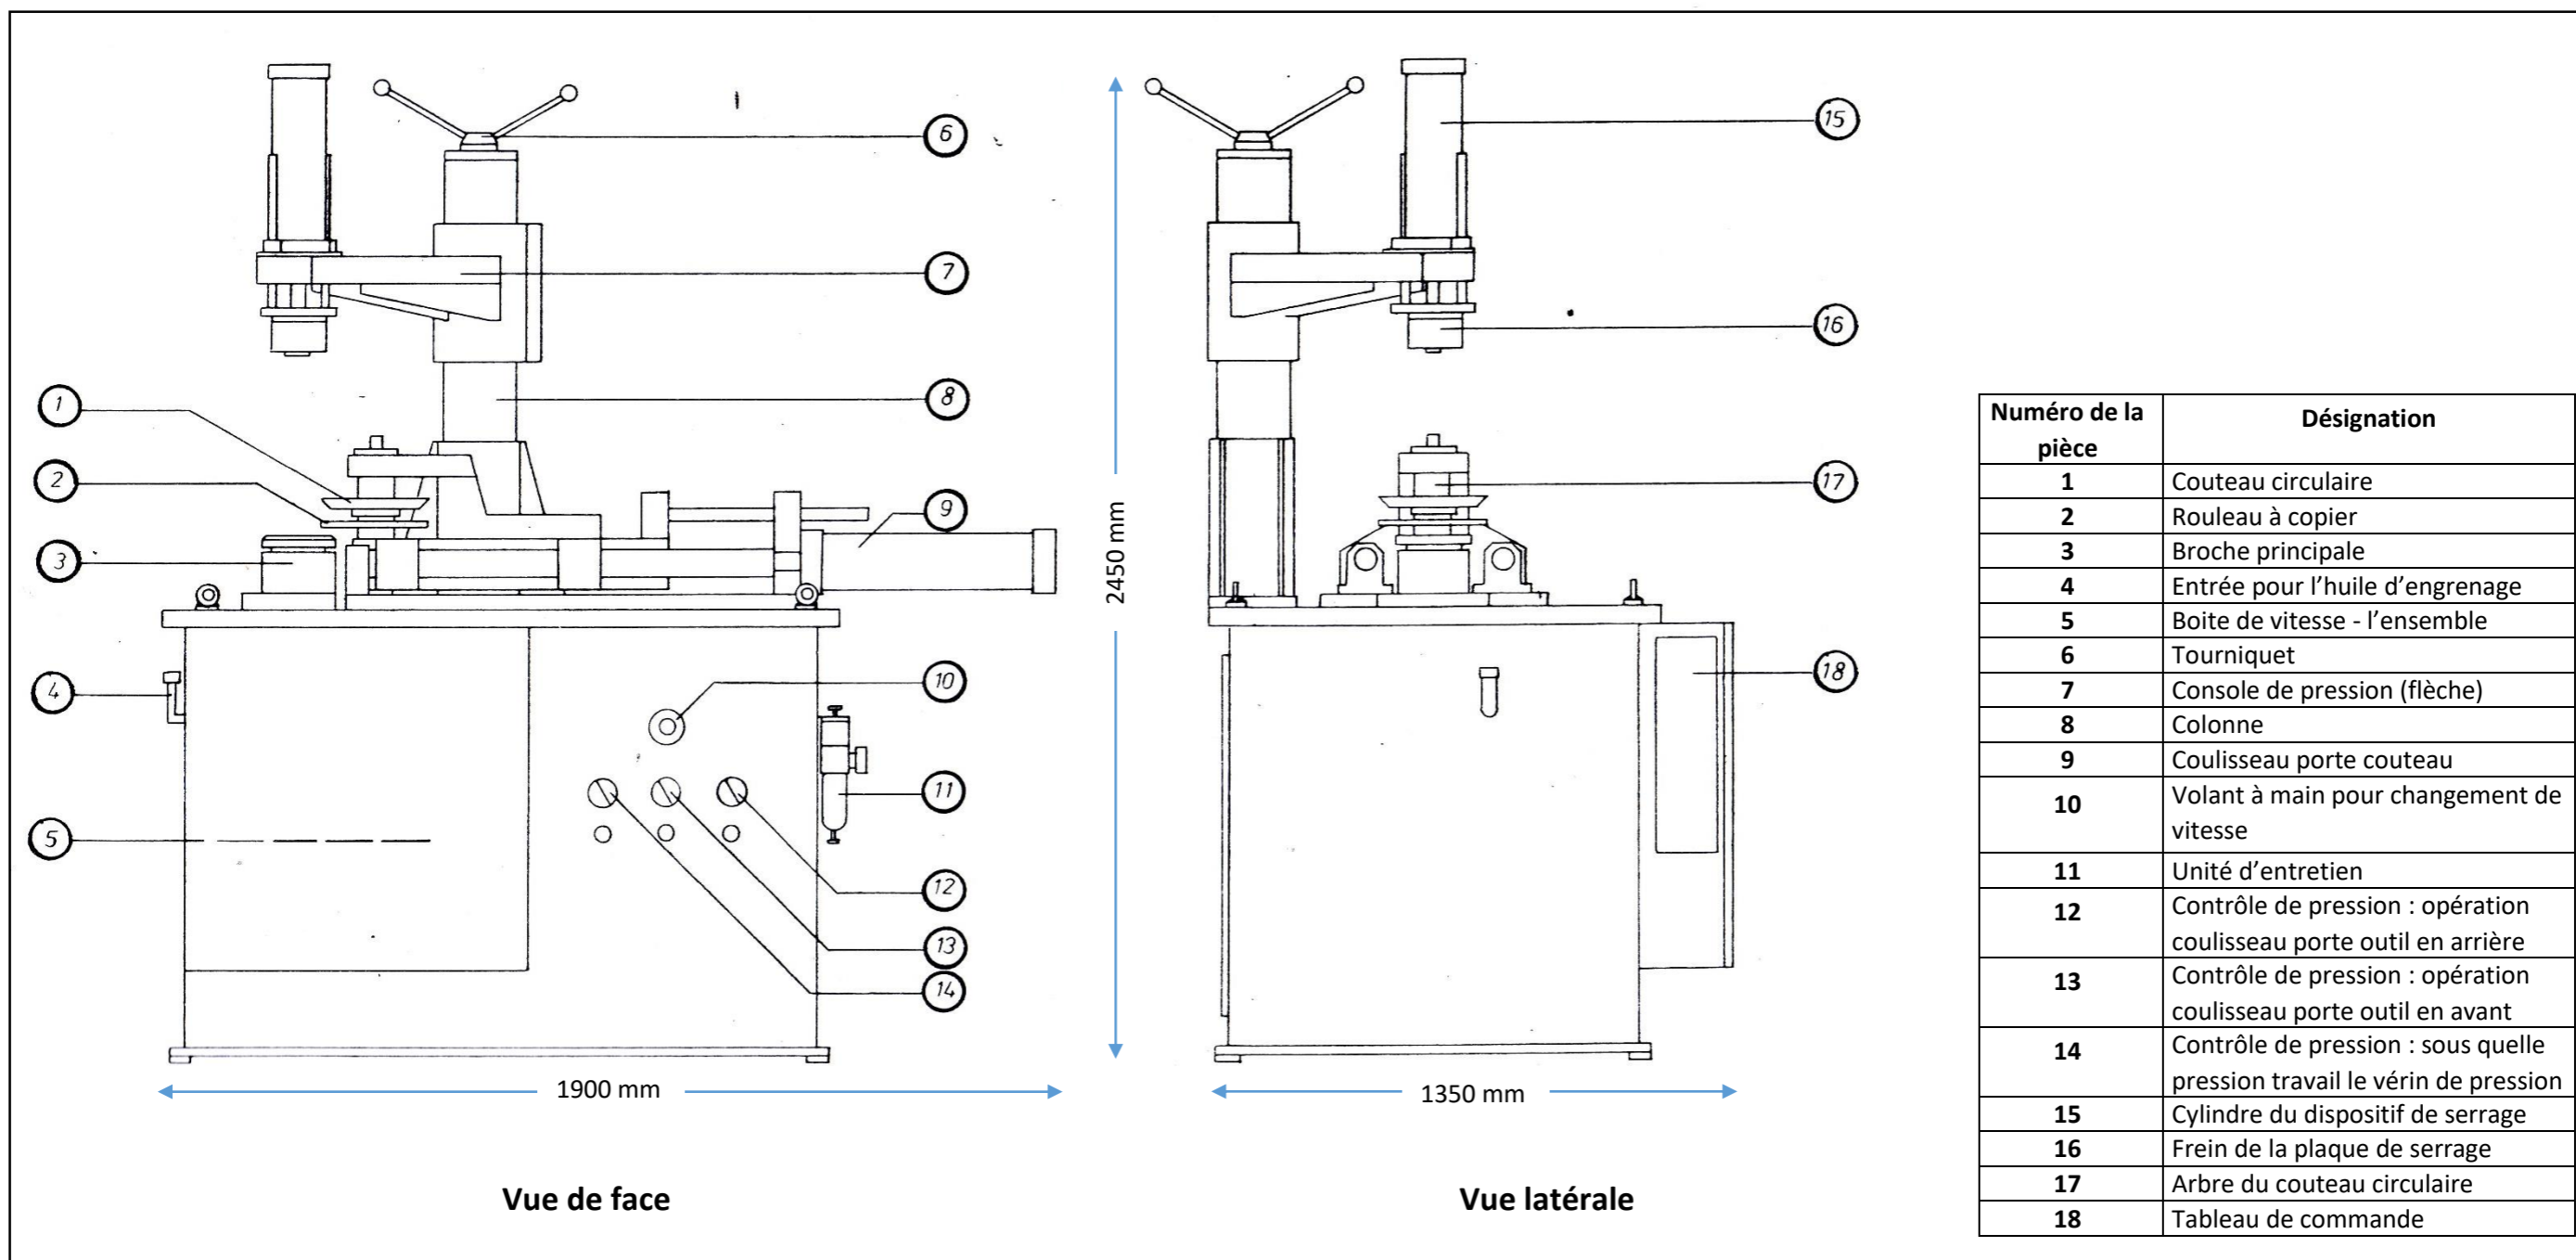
Dessin d'ensemble de la machine à détourer type BSU 650.
